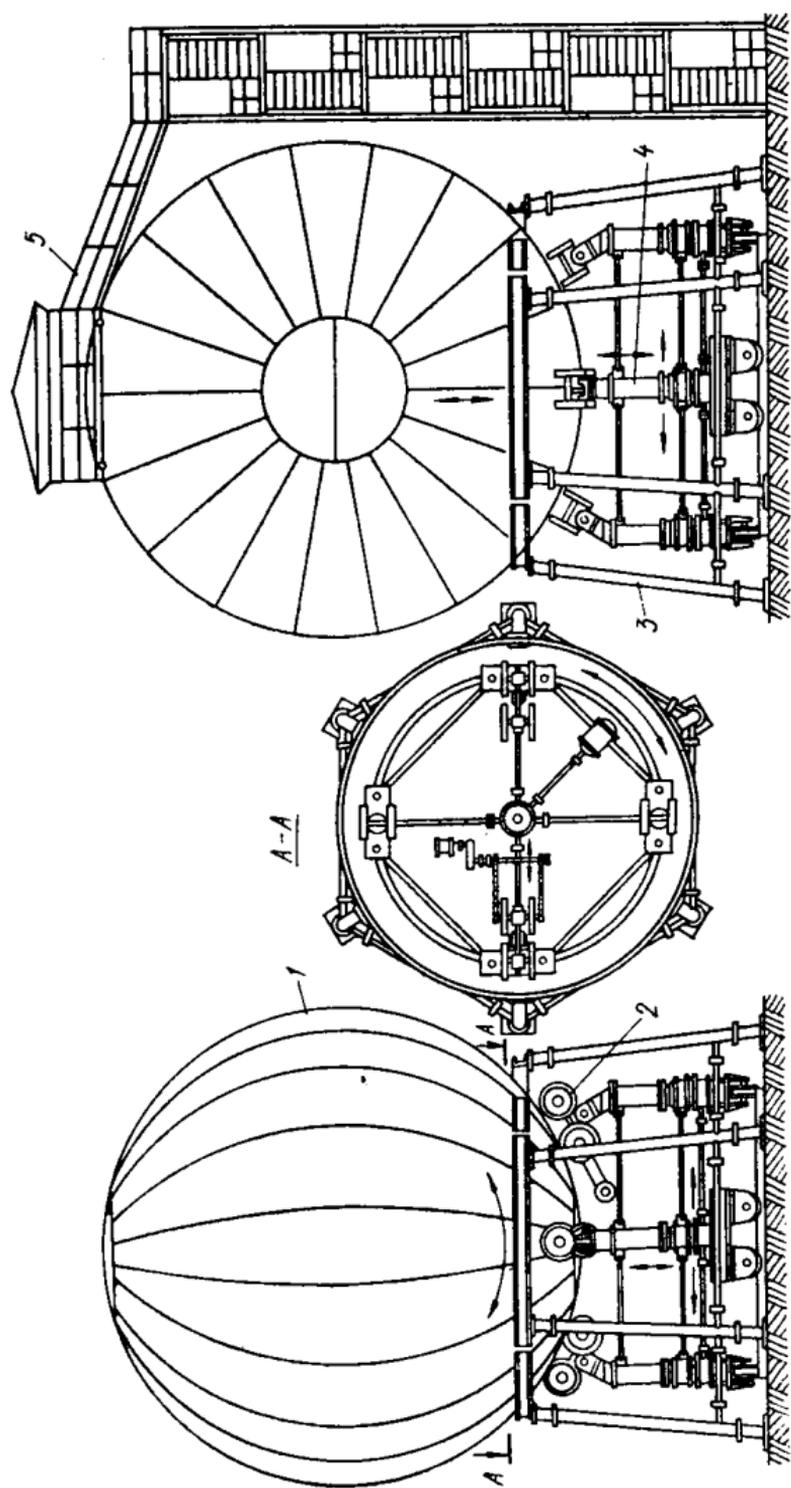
Установка для сварки резервуаров емкостью 600 м^3 с манипулятором конструкции Г. С. Сабирова:
